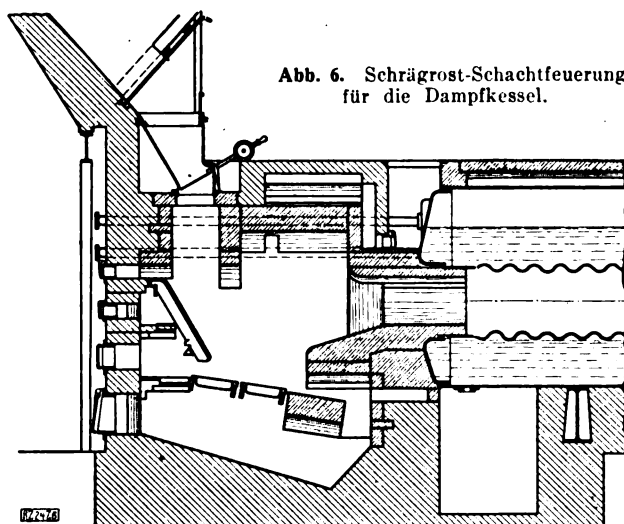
Schrägrost-Schachtfeuerung für die Dampfkessel.
